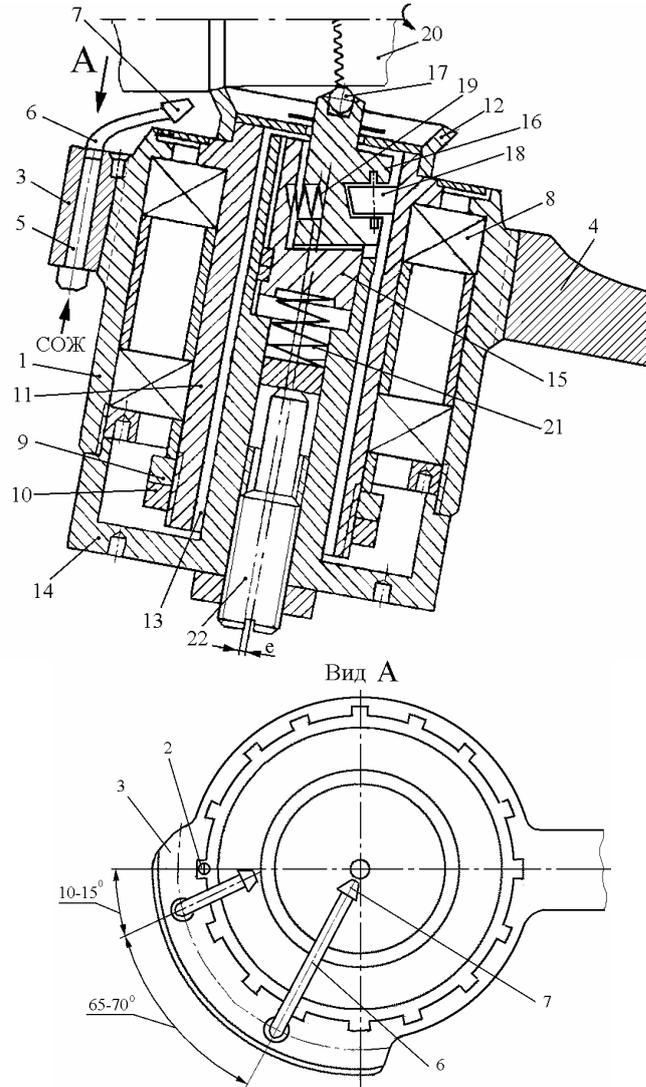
Многофункциональное устройство для режуще-деформирующей обработки с нанесением антифрикционных покрытий: 1 – корпус; 2 – штифт резьбовой; 3 – приспособление; 4 – хвостовик; 5 – отверстие сквозное; 6 – трубка; 7 – сопло дозирующее; 8 – подшипниковая опора; 9, 10 – гайка; 11 – державка; 12 – резец; 13 – отверстие; 14 – направляющая втулка; 15 – стакан; 16 – опора; 17 – шарик; 18 – ролик конический; 19 – пружина; 20 – заготовка; 21 – пружина тарированная; 22 – винт
